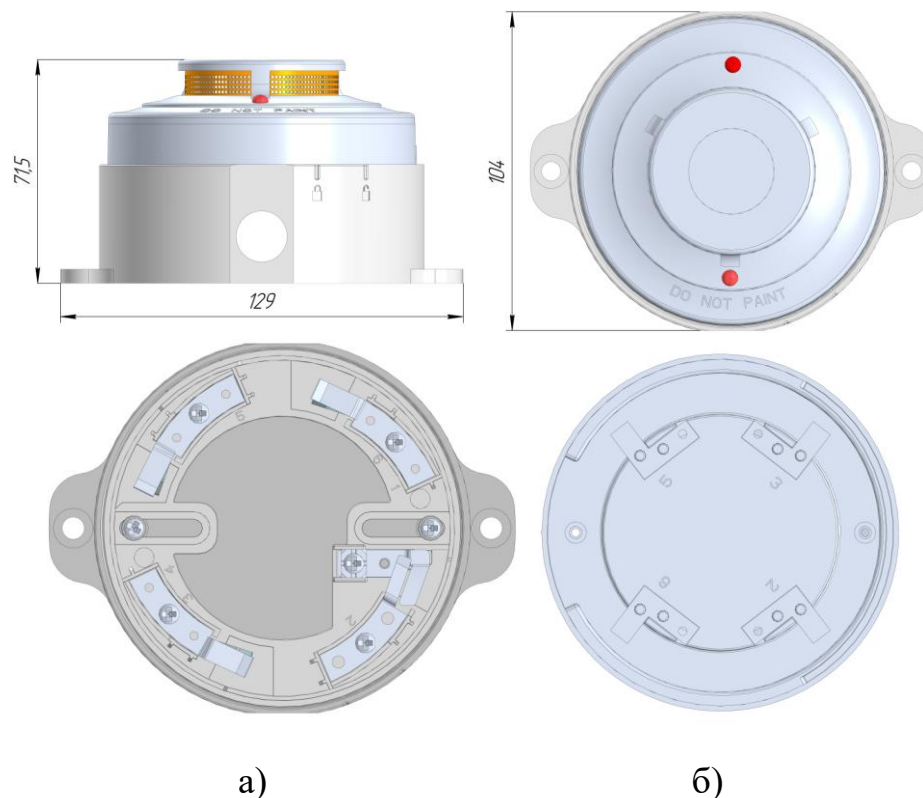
Общий вид извещателя пожарного дымового адресного «СПАРК» ИП212-01В а) высокое базовое основание б) корпус
